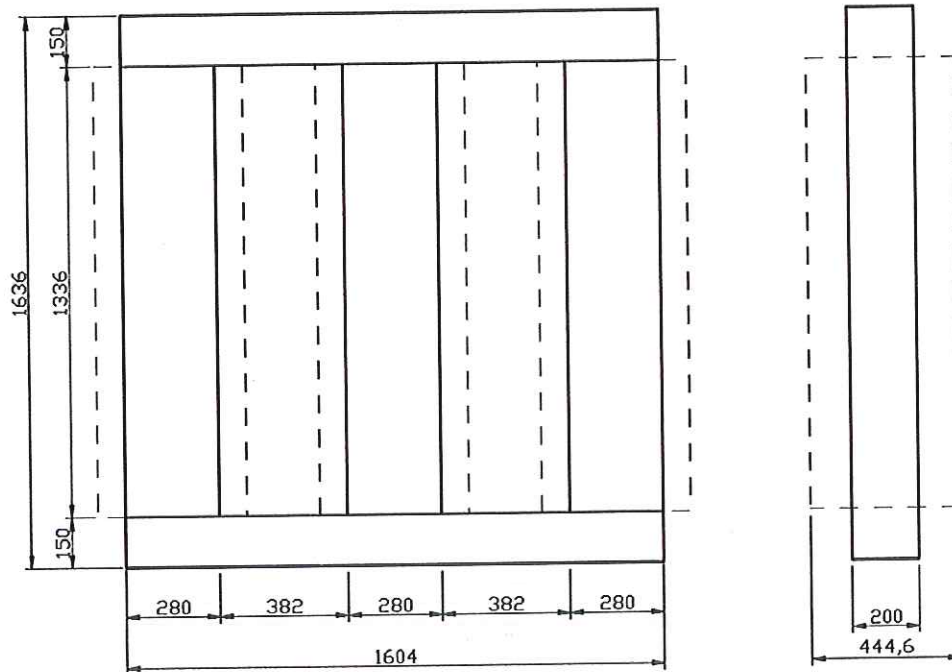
Dimensões do Núcleo e das bobinas do transformador de 1.000kVA
